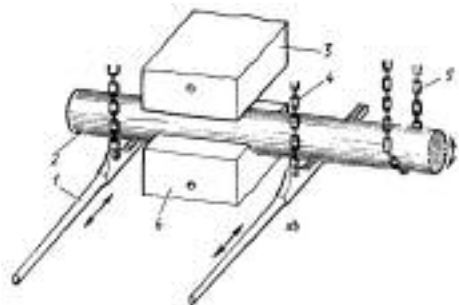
Приспособления для поворачивания заготовок при ковке на молотах:
